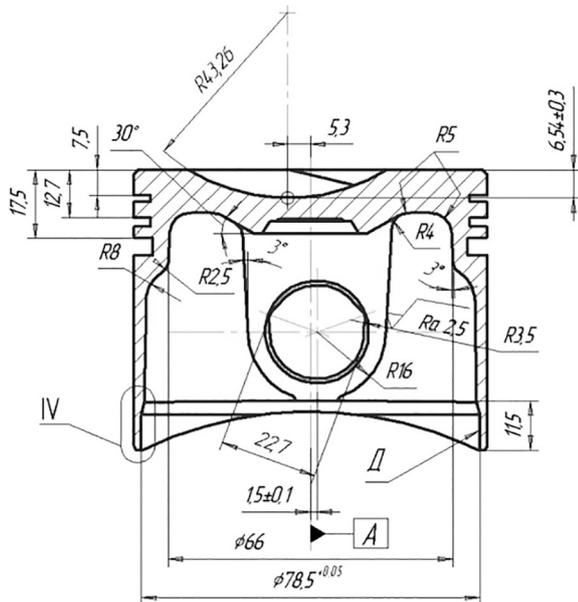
Чертеж и общий вид поршня двигателя легкового автомобиля ВАЗ 21124
